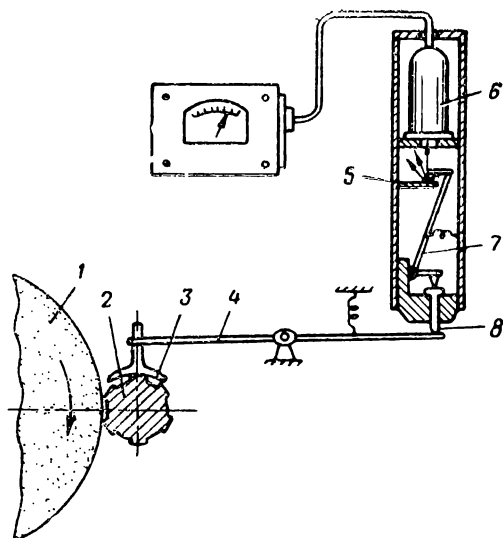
Схема прибора с радиоактивным веществом для контроля обработки шлифованием:
